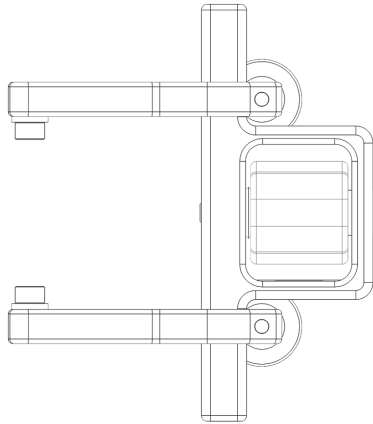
Короткая вилка для призмы мин. ширины (31,75 мм)
